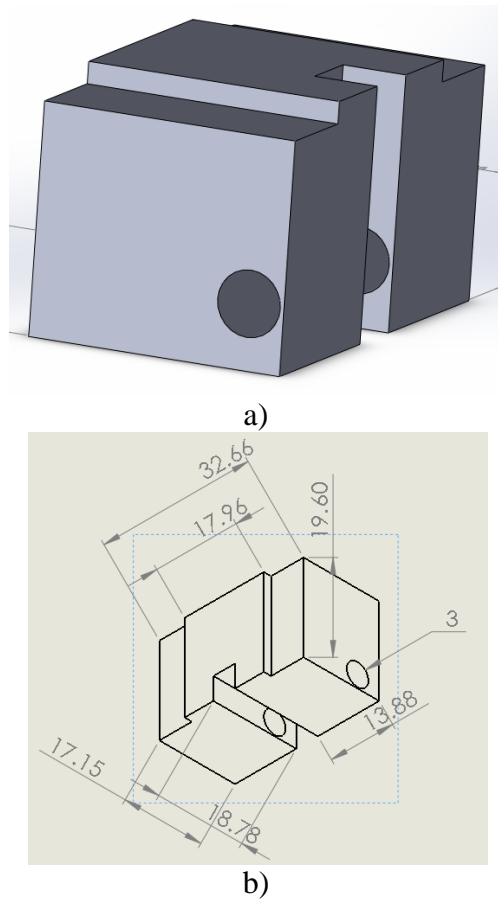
Manivela: a) Pieza terminada; b) Dimensiones. Fuente: Autor.
